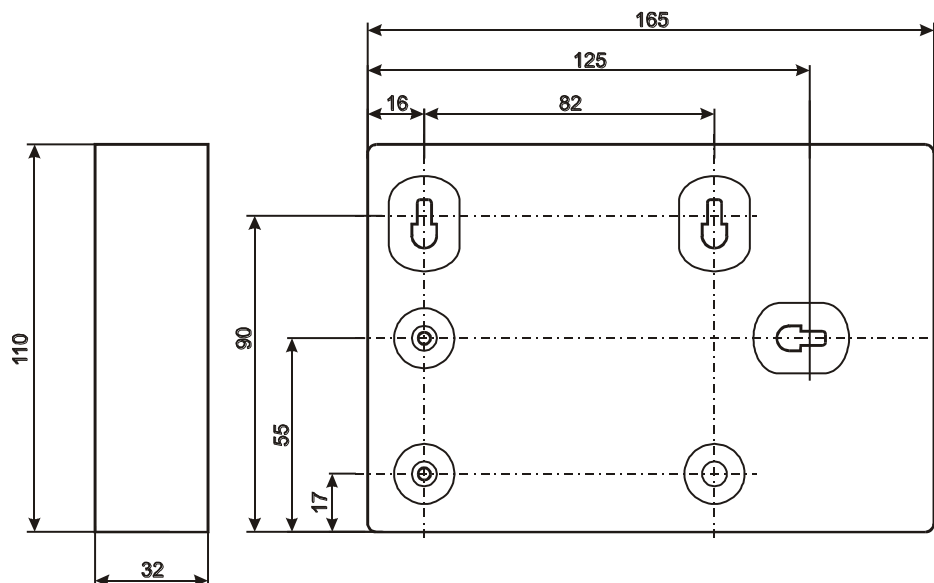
Внешний вид и габаритные размеры БРЛ в исп. IP20
